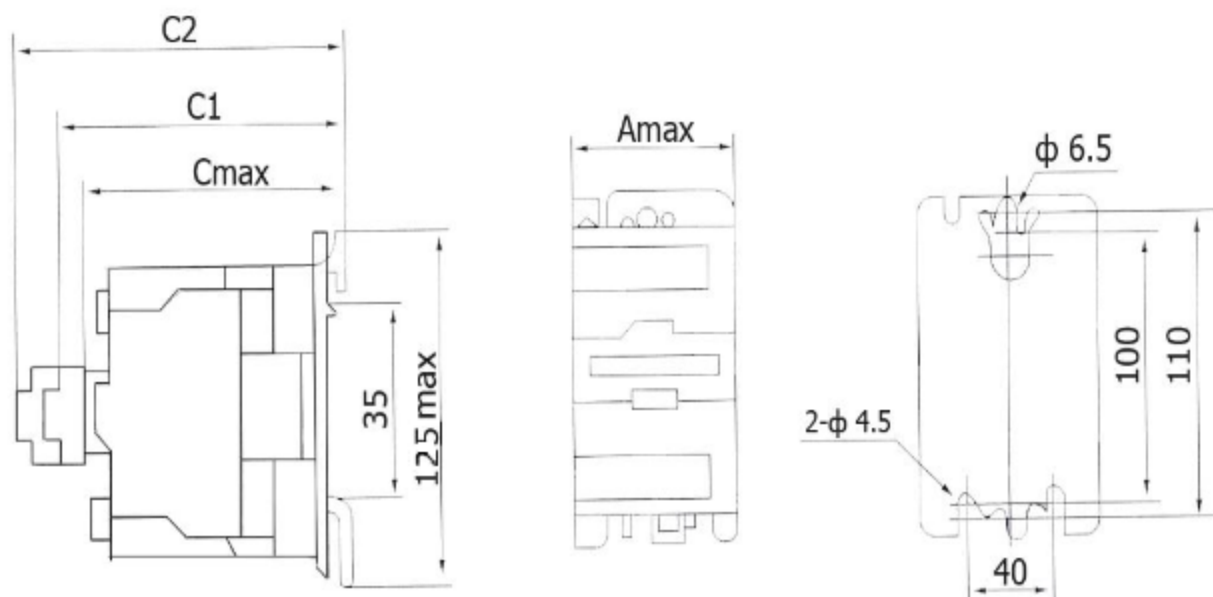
Габаритные и присоединительные размеры пускателей 40-100А
